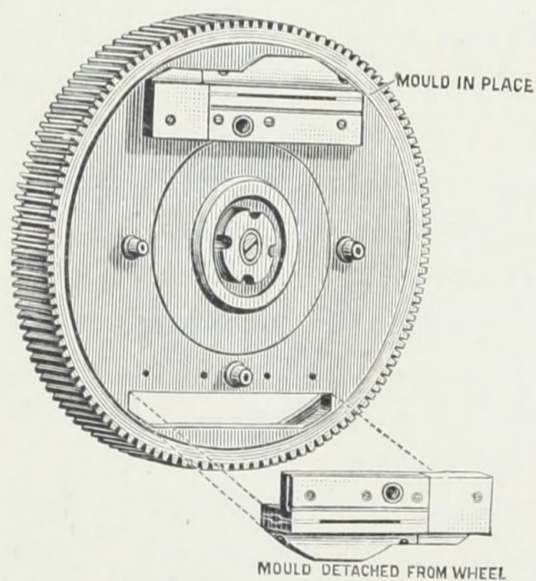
Mould in place = Støbeinstrumentet paa Plads. Mould detached from Wheel = Støbeinstrumentet skilt fra Hjulet.
